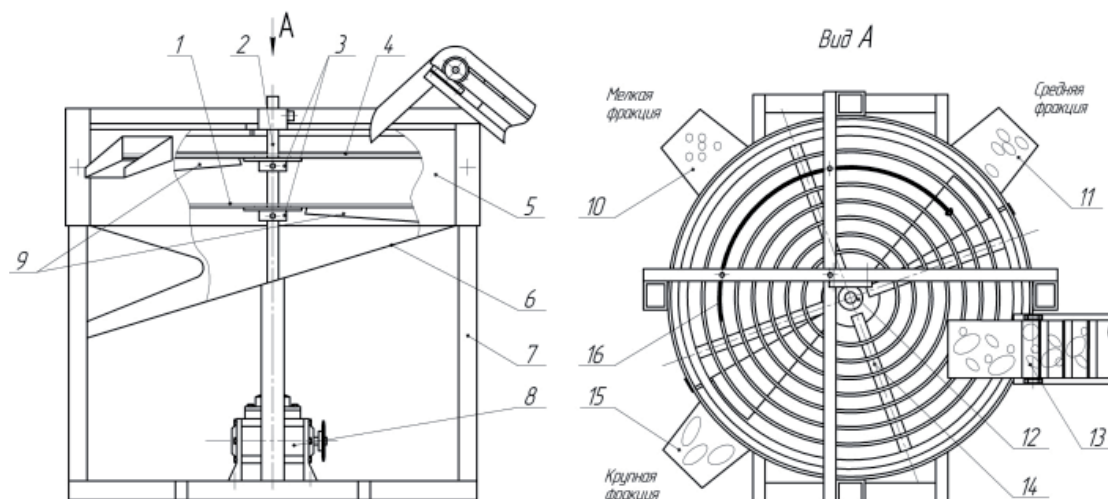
Общий вид чашечно-дисковой сортировки: 1 – второе решето; 2 – вал; 3 – ступица; 4 – первое решето; 5 – обод кожуха; 6 – приемник; 7 – рама; 8 – редуктор; 9 – подъемная планка; 10 – выгрузной лоток мелкой фракции; 11 – выгрузной лоток средней фракции; 12 – подшипник; 13 – питающий транспортер; 14 – спица; 15 – выгрузной лоток крупной фракции; 16 – сектор-обод
